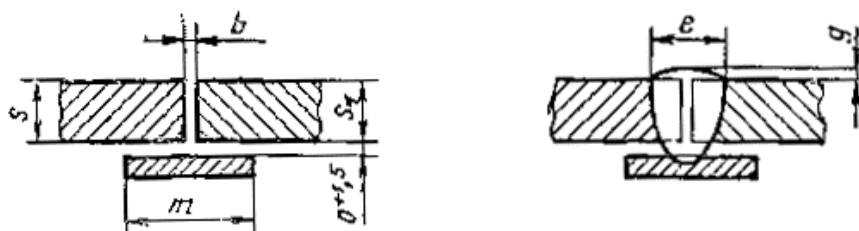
Сварное соединение С5 ГОСТ 14771-76 для сварки кольцевого шва
